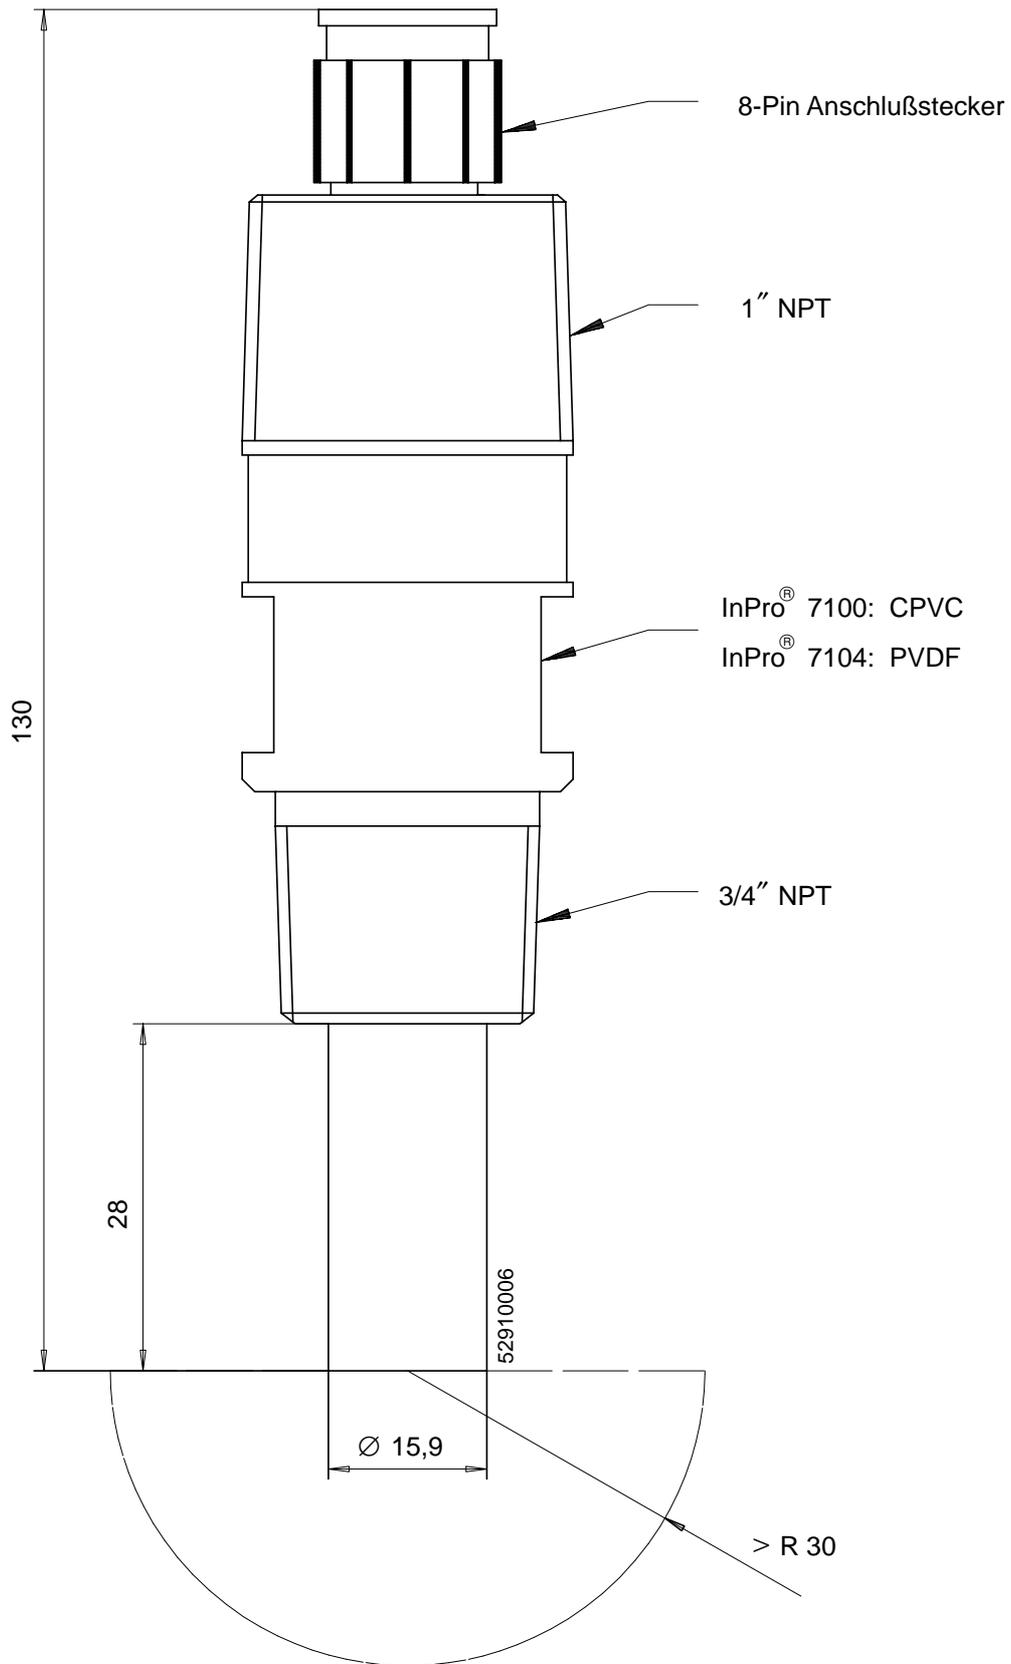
Maßzeichnung InPro[®] 7100 / 7104
